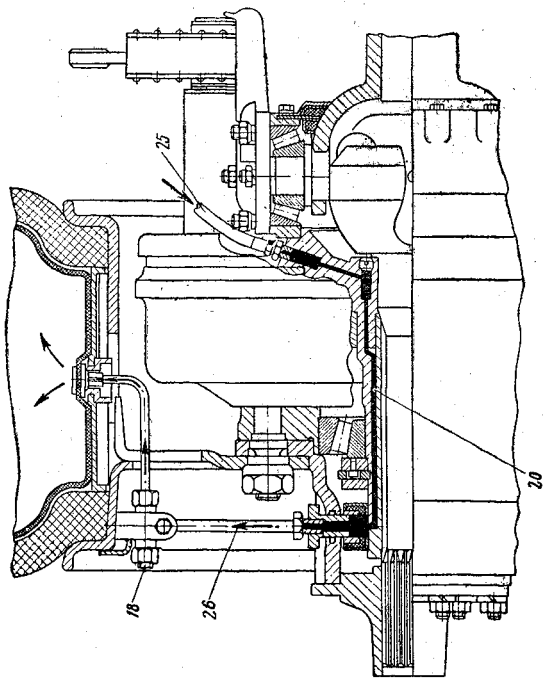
Схема подвода воздуха к шине колеса через цапфу; что на рис. 58; 25 — шланг подвода воздуха; 26 — трубка подвода воздуха
